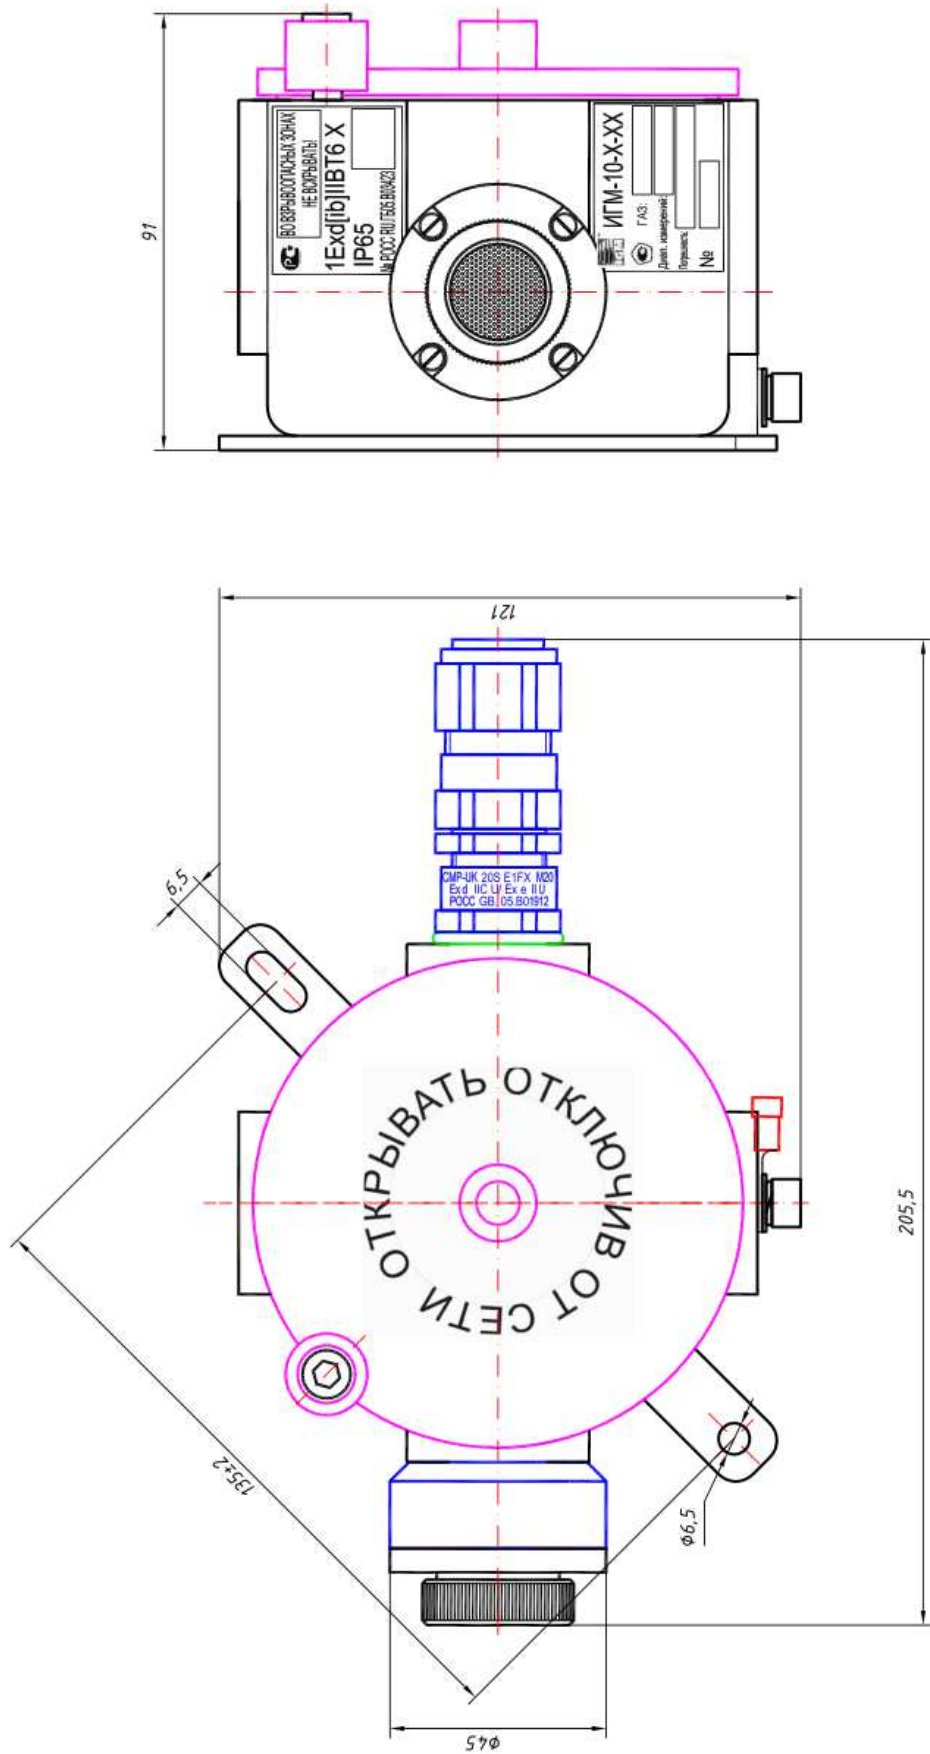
Габаритный чертеж ИГМ-10-Х-11.
